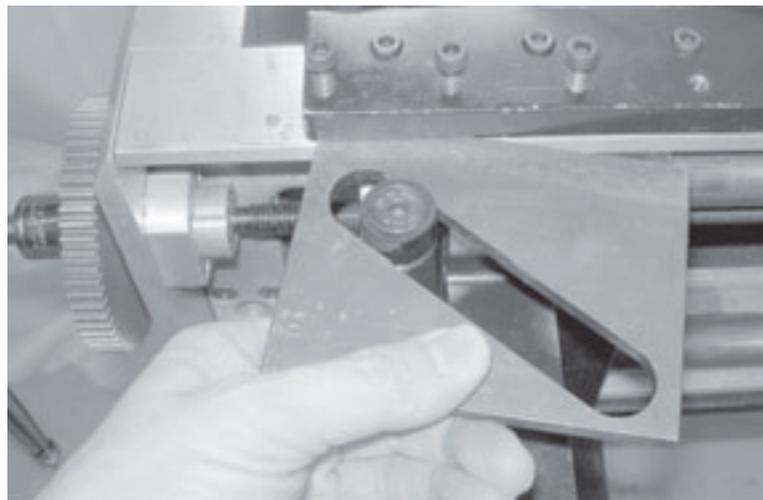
Drehen Sie die Kronenmutter, um die Spitze gerade hinter dem Rohraußendurchmesser zu positionieren.
